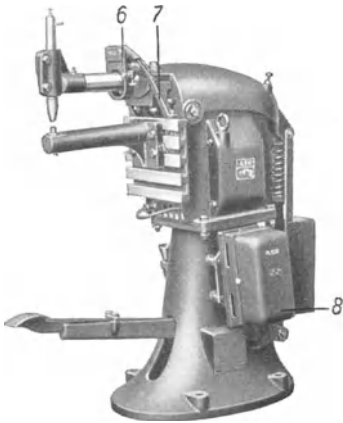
Punktschweißmaschine mit Kontroller.
